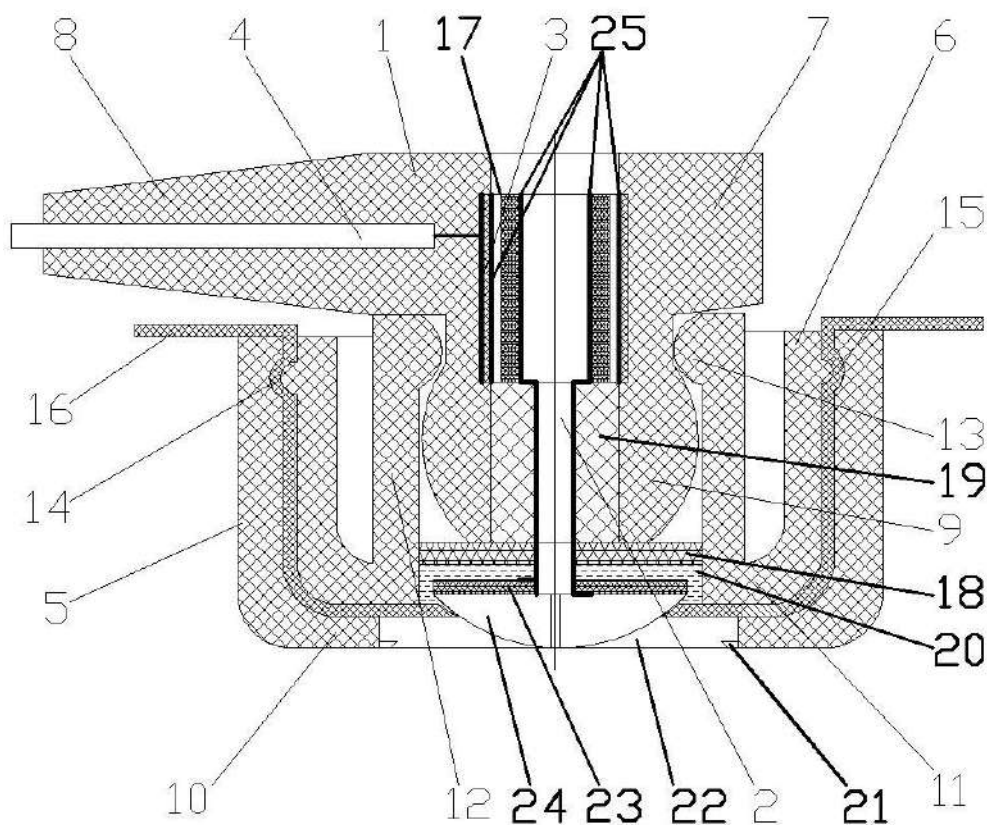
Універсальний датчик з пьезоперетворювачем, де 1 - корпус електрода; 2 - порожнина для заповнення гелем; 3 - струмознімач; 4 - провідник; 5- підстава настановного гнізда; 6 - вкладиш установочного гнізда; 7 - фланець корпусу електрода; 8 - гофрований хвостовик; 9 - кулясте стовщення на торці корпусу електрода; 10 - полка відбортовки основи установочного гнізда; 11 - полка відбортовки вкладиша установочного гнізда; 12 - цангова засувка вкладиша установочного гнізда; 13 - буртик на торці цангової засувки; 14 - поясок на зовнішній поверхні вкладиша настановного гнізда; 15 - канавка на внутрішній поверхні основи настановного гнізда; 16 - тканина тримача електродів; 17 - втулка; 18 - прокладка; 19 - демпфер; 20 - узгоджуючий шар; 21 - тримач п'єзоперетворювача; 22 - захисний ковпак 23 - п'єзоелемент; 24- акустична лінза; 25 - контакти.
